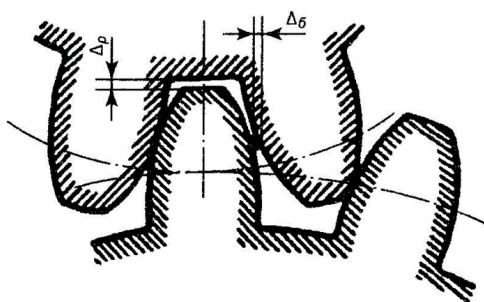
Схема розташування радіального (Др) і бічного (Дб) зазорів в циліндричній зубчастій передачі
